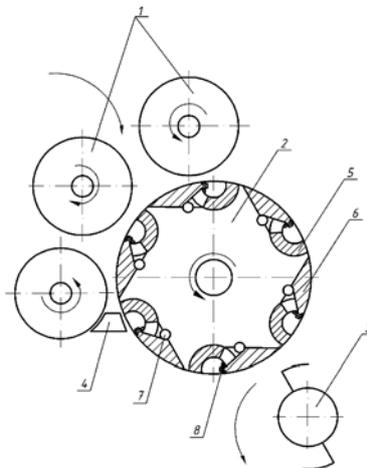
Механізм поділу тіста на заготовки ділильно-закатувальної машини А2-ХБУ
